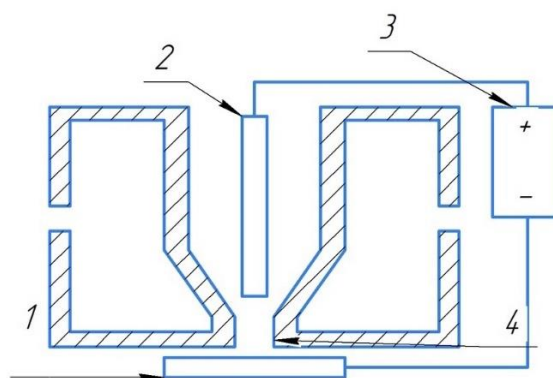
Схема при сварке на прямой полярности
